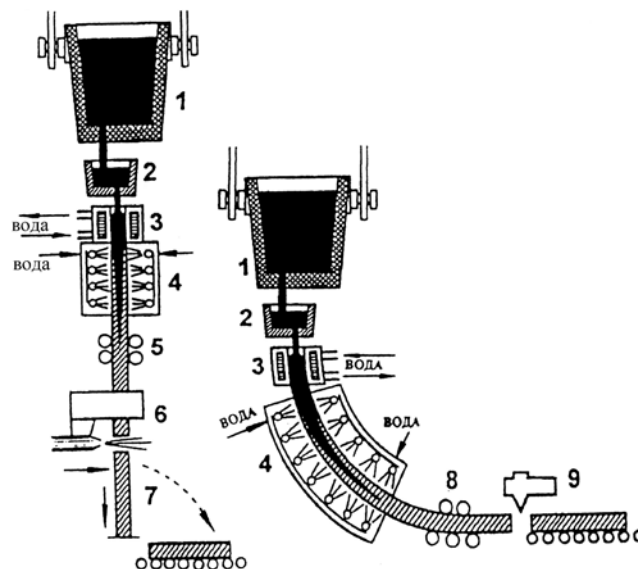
Схема установки безперервного лиття заготовок вертикального типу та з подальшим згином зливка:
